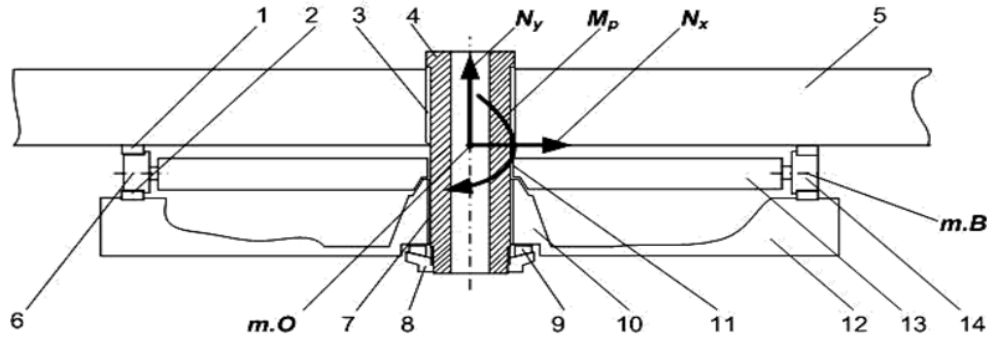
Схема общей конструкции опорно-поворотного устройства и расположения реакций связей: 1 – верхний рельс, 2 – нижний рельс, 3 – втулка (верхний и нижний пояса) поворотной платформы, 4 – центральная цапфа, 5 – поворотная платформа, 6 – роликовый круг, 7 – втулка нижней рамы, 8 – гайка центральной цапфы, 9 – сферическая шайба, 10 – отливка нижней рамы, 11 – втулка сепаратора роликового круга, 12 – нижняя рама, 13 – сепаратор роликового круга, 14 – передний ролик (точка В), N_x – горизонтальная составляющая нагрузок, N_y – вертикальная составляющая нагрузок, M_p – реактивный (изгибающий) момент.
